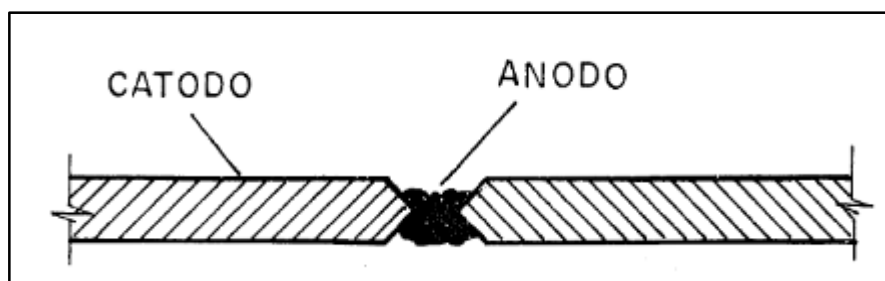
Unión soldada actuando como ánodo respecto al material base.
